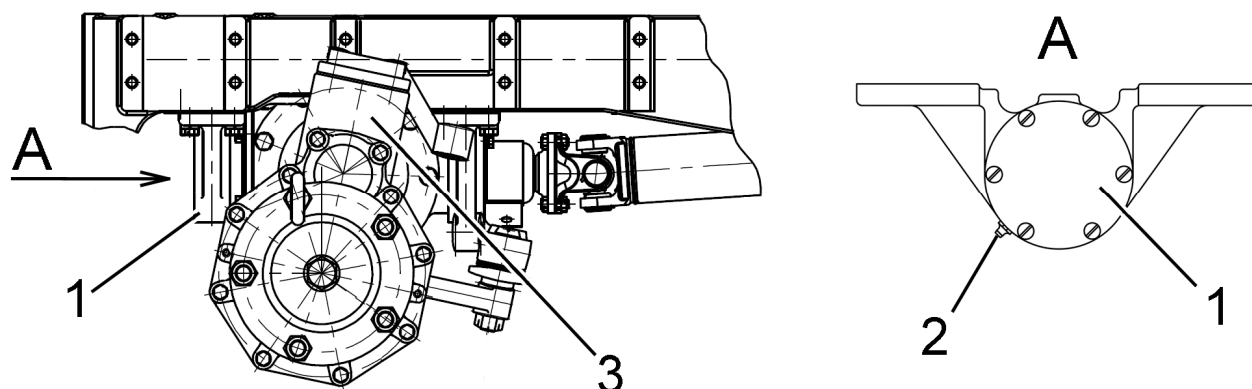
Проверка уровня масла в корпусах колесных редукторов ПВМ
